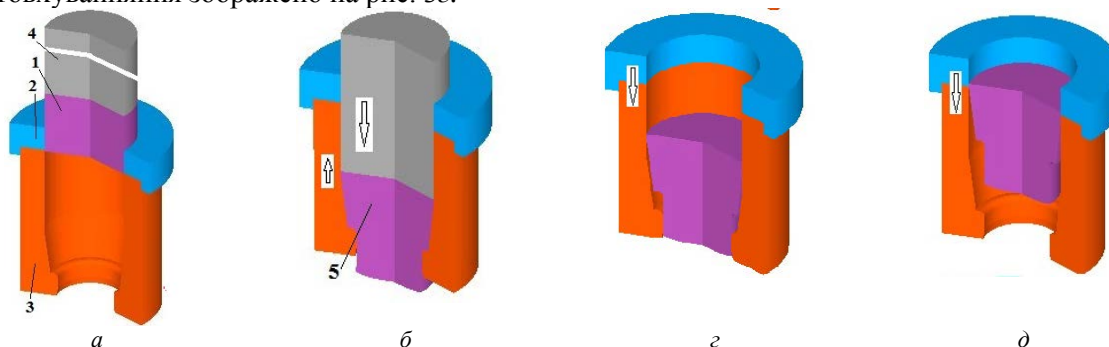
Розрахункові положення заготовки і деформуючого інструмента при видавлюванні: а – після встановлення заготовки (1 – заготовка, 2 – направляюче кільце, 3 – контейнер, 4 – пуансон), б – в кінці видавлювання (5 – деформована заготовка), в – на проміжній стадії виштовхування деформованої заготовки, г – в кінці виштовхування
